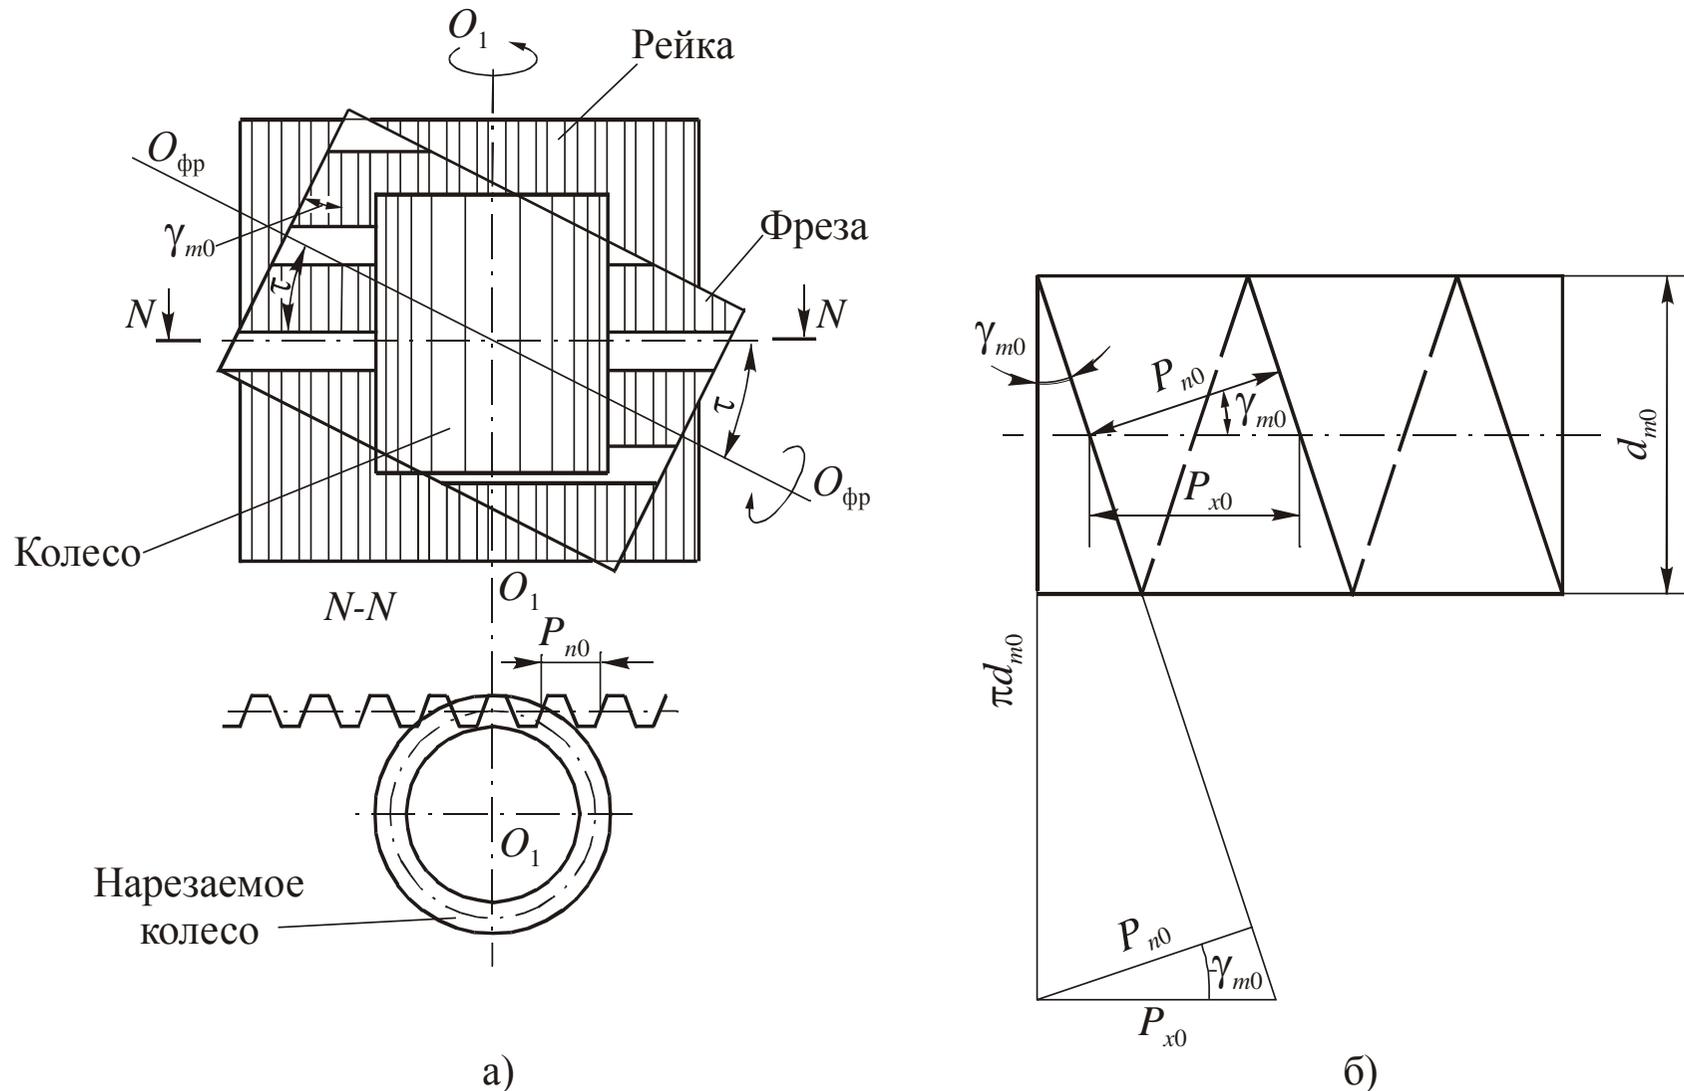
Схема зубонарезания червячной фрезой: а – зацепление колеса и фрезы с рейкой; б – развертка витка фрезы на делительном цилиндре
